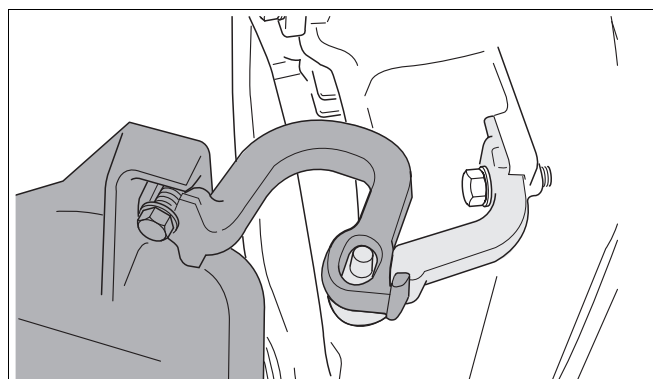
Montaggio della porta del bruciatore (qui: a destra)
